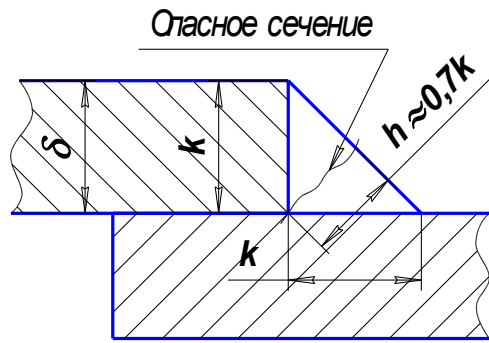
Геометрия углового сварного шва
